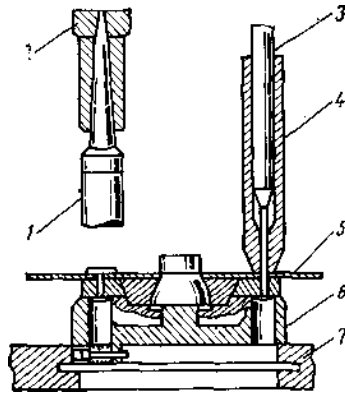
Видалення заклепок за допомогою кінцевої фрези і бородки:
